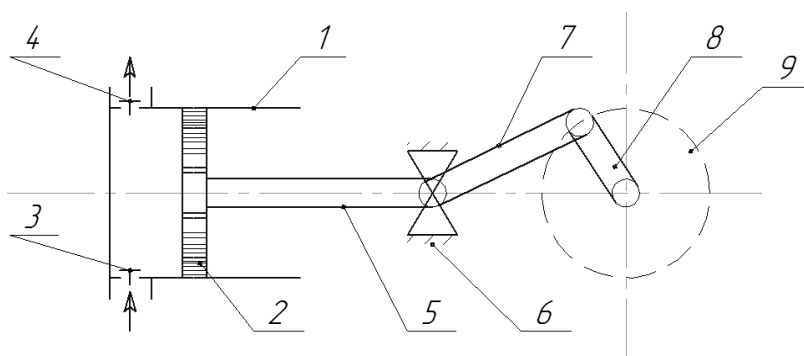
Поршневой насос простого действия: 1 – цилиндр; 2 – поршень; 3 – всасывающий клапан; 4 – нагнетательный клапан; 5 – шток; 6 – ползун; 7 – шатун; 8 – кривошип; 9 – маховик
